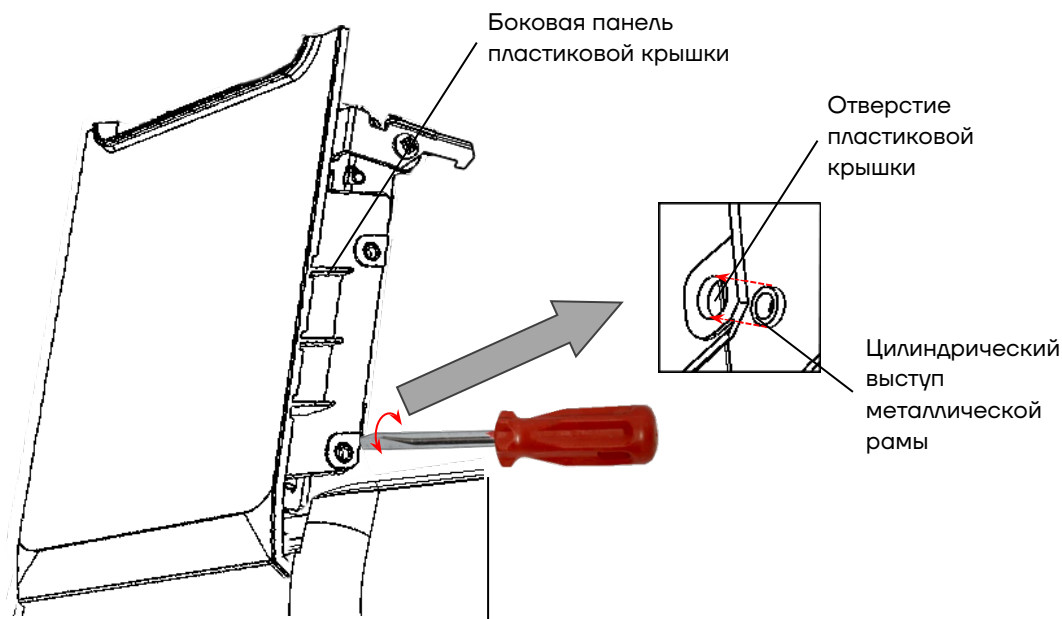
Отделение пластиковой крышки от металлической рамы печатающего устройства
